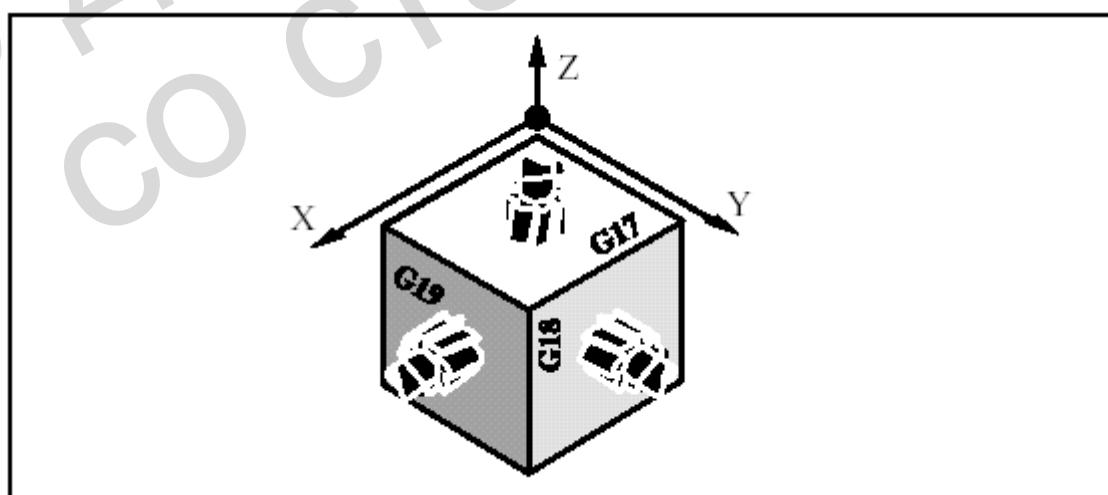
Плоскости и привязки осей при сверлении/фрезеровании
